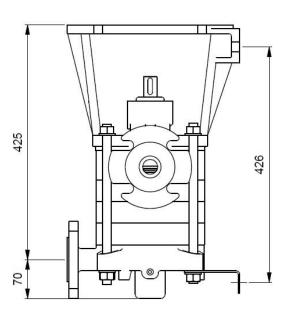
Габаритный чертеж насоса TSL 32/4 и присоединительные размеры
